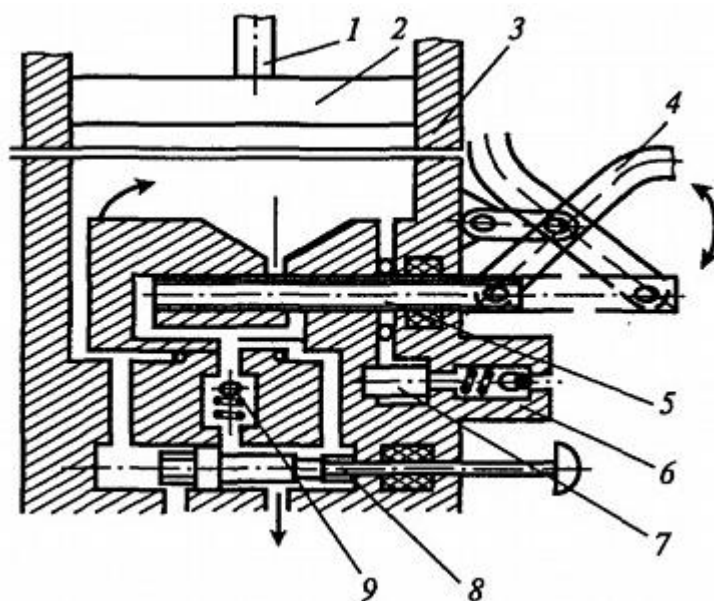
Схема ручной централизованной смазочной станции СРГ: 1 — указатель уровня; 2 — поршень; 3 — резервуар смазки; 4 — рычаг; 5 — насос; 7 — сетчатый фильтр; 6, 8 и 9 — заправочный, переключающий и обратный
